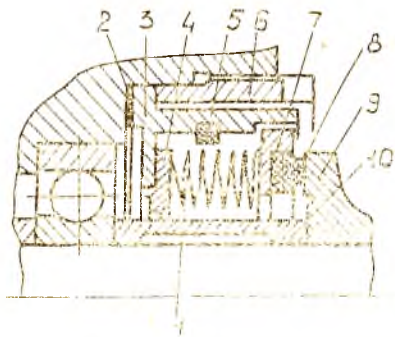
Конструкция ТКУ со сварным сильфоном
